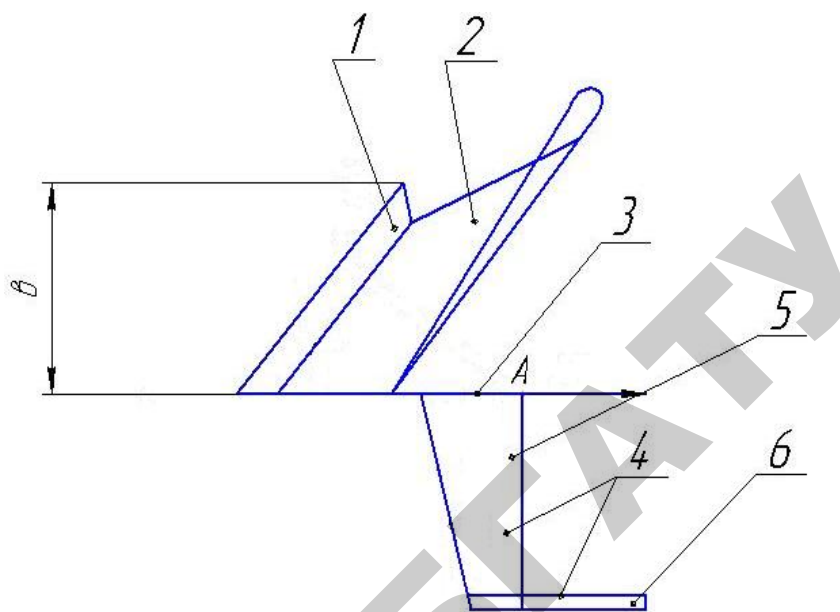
Схема сил, действующих на предлагаемый корпус плуга: 1 – лемех; 2 – отвал; 3 – полевая доска; 4 – комбинированный нож, состоящий из горизонтального 5 и вертикального 6 (типа «акулий плавник») ножей; b – ширина захвата корпуса
